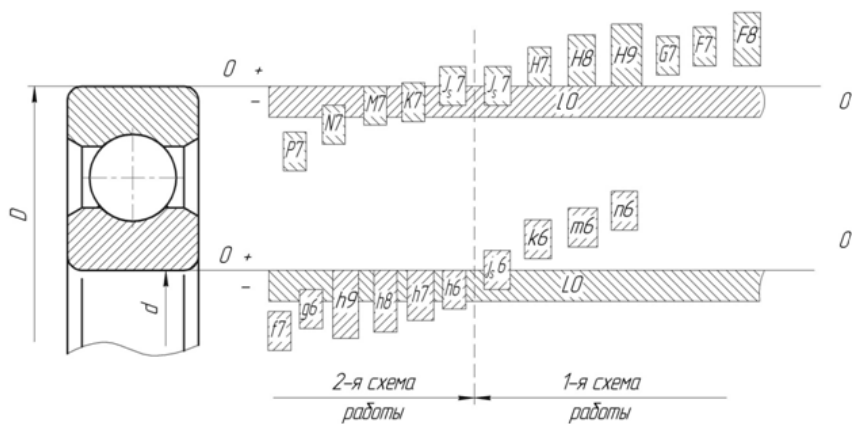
Схема расположения интервалов допусков при посадках подшипников нормального класса точности
